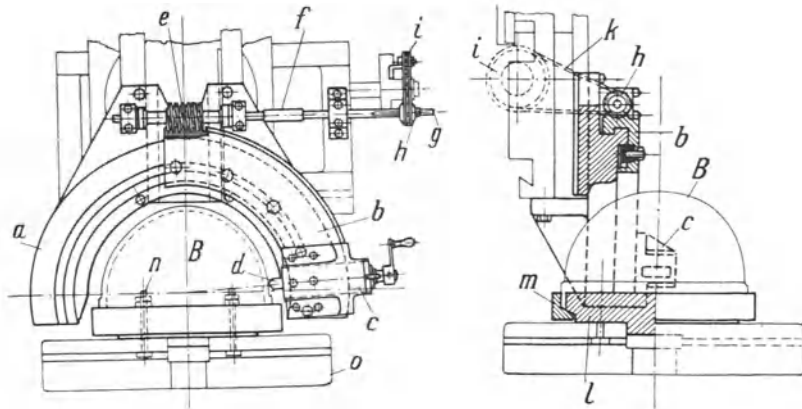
Halbkugeldrehvorrichtung für große gußeiserne Kappen.
